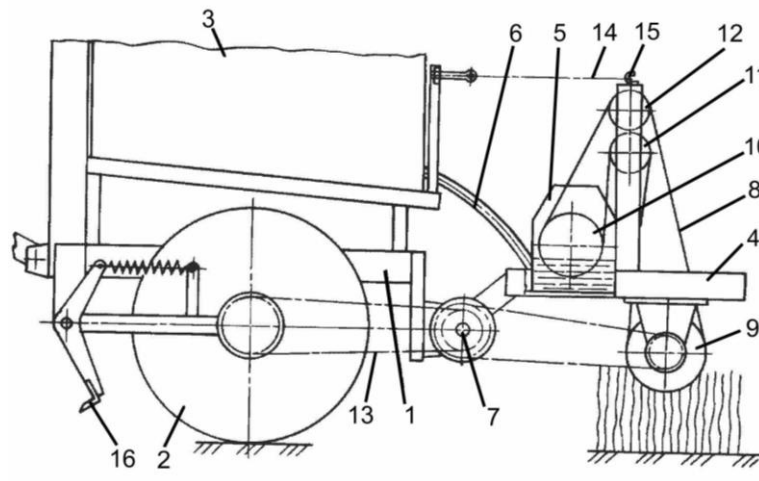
Схема машини для нанесення отрутохімікатів на рослини: 1 - основна рама; 2 - приводне колесо; 3 - резервуар; 4 - допоміжна рама; 5 - робочий резервуар; 6 - трубовід; 7 - проміжний вал; 8 - полотно; 9 - робочий валик; 10 - валик резервуару; 11; 12 - допоміжні валики; 13 - приводний ланцюг; 14 - натажний ланцюг; 15 - крюк; 16 - скарифікатор
